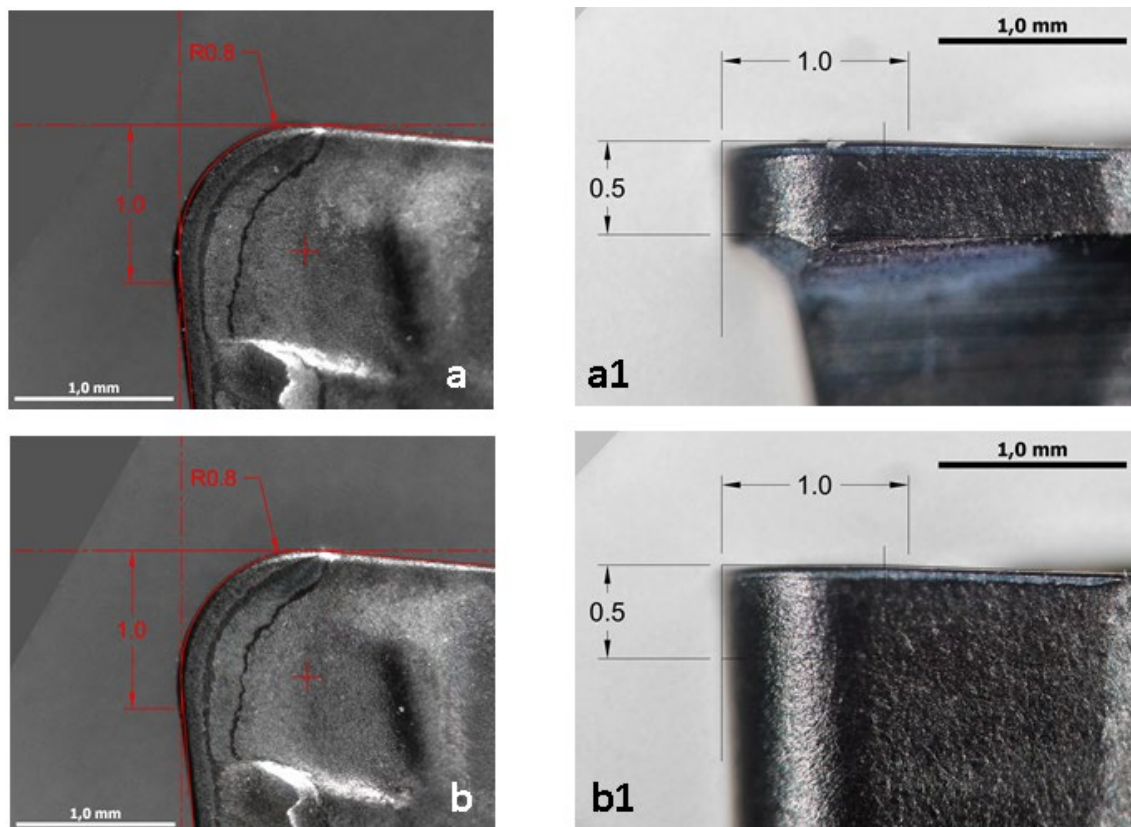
Insertos após usinagem com profundidade de usinagem 2,5mm e limpos com banho químico: (a) I8-M e (b) I8-N.
